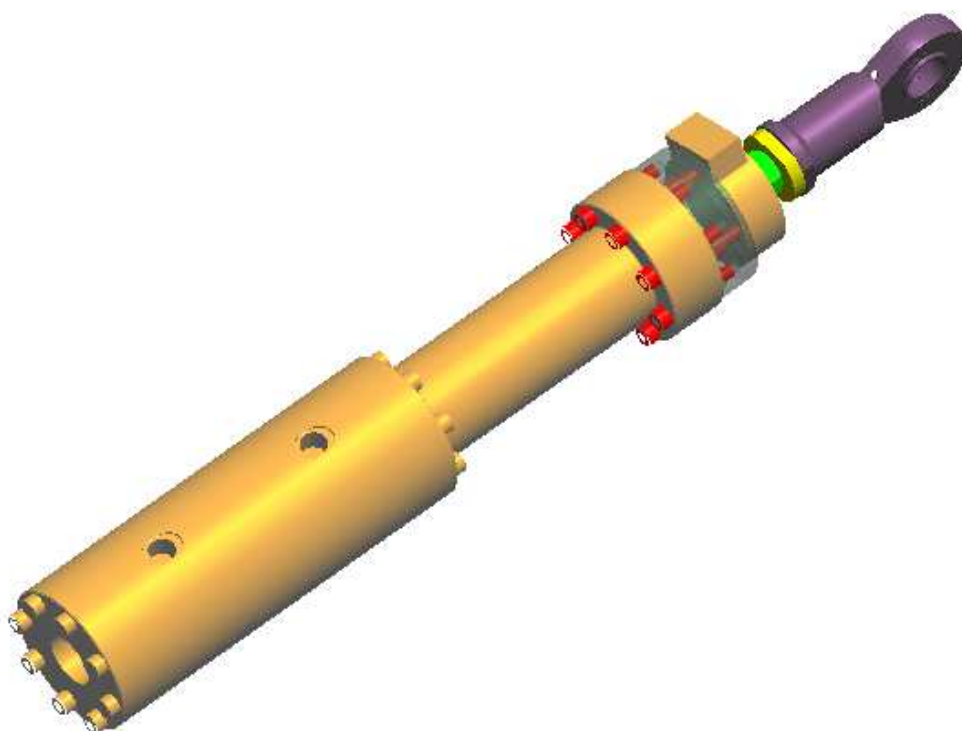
Setrvačné hmoty horní části uložení zjištěné v Pro ENGINEERu
